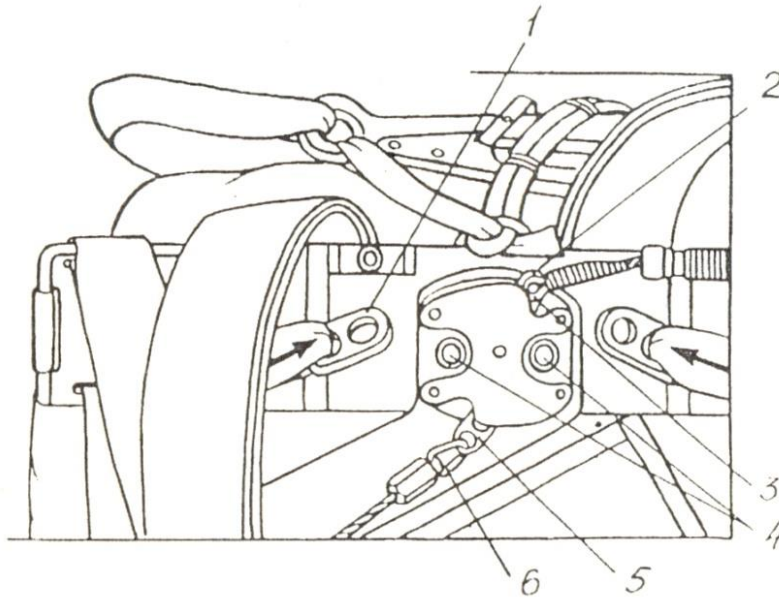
Монтаж петли троса звена ручного раскрытия, серьги и пряжек силовых лент на двухконусный замок:
